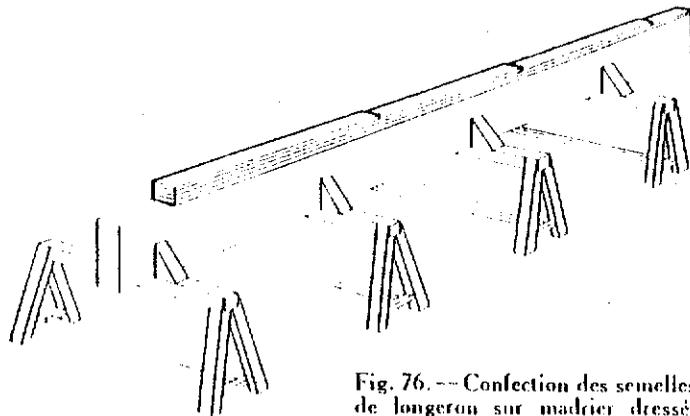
Confection des semelles de longeron sur madrier dressé.
